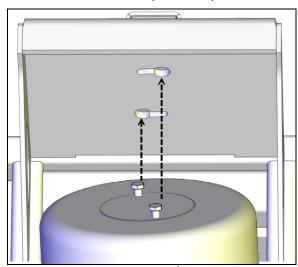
PLAQUE DE MONTAGE SUPÉRIEURE DE RESSORT PNEUMATIQUE
